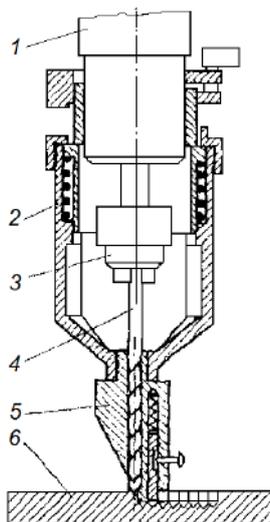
Схема сверления отверстий по кондуктору
